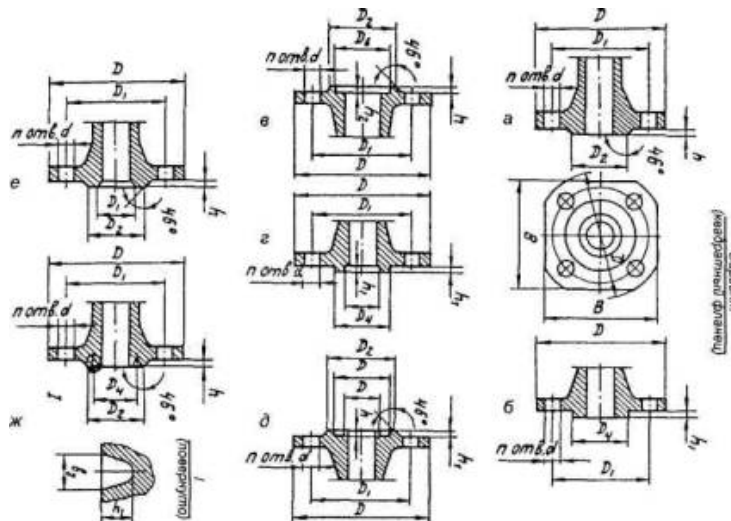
Типы и уплотнительные поверхности фланцев технологических трубопроводов: а - с соединительным выступом; б - с выступом; в - с впадиной; г - с шипом; д - с пазом; е - под линзовую прокладку; ж - под прокладку овального сечения
